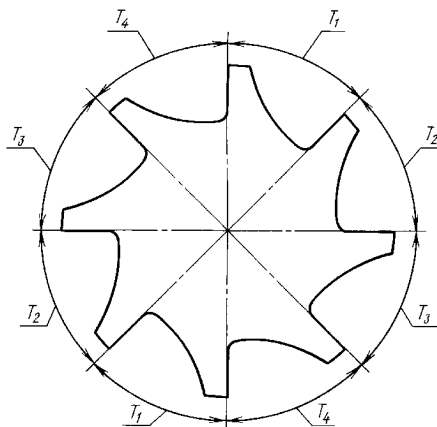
Неравномерная разбивка угловых шагов зубьев развертки
